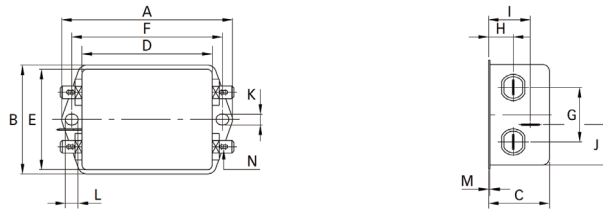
Габаритный чертеж фильтров серии FN 2090 (ед. изм.: мм)
